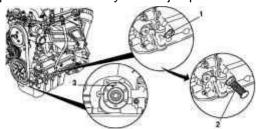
Поворачивание коленчатого вала: 1 – болт; 2 – специальный инструмент; 3 – метка
